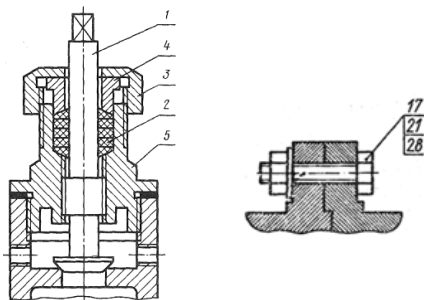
Расположение номеров позиций для группы деталей
